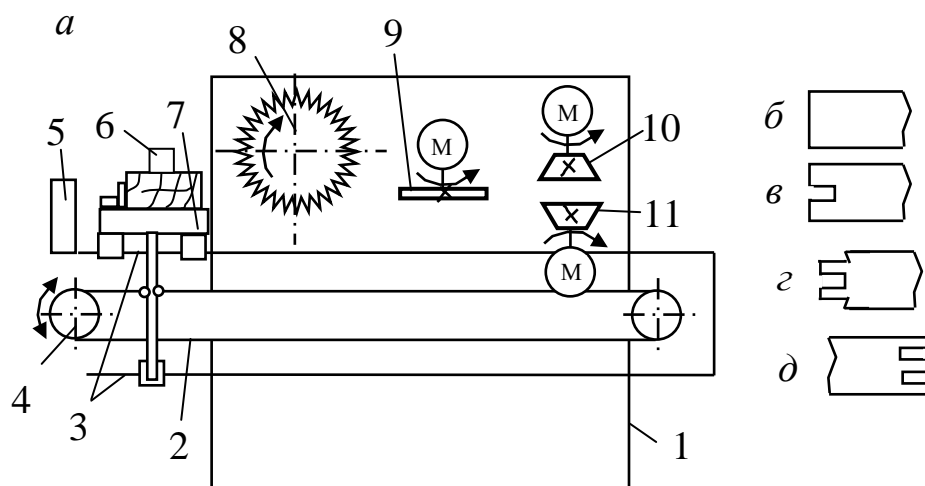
Односторонний рамный шипорезный станок ШО15Г-5: а – технологическая схема; б – заготовка после обработки пилой; в – заготовка после обработки проушечным диском; г – готовые концы детали; д –
